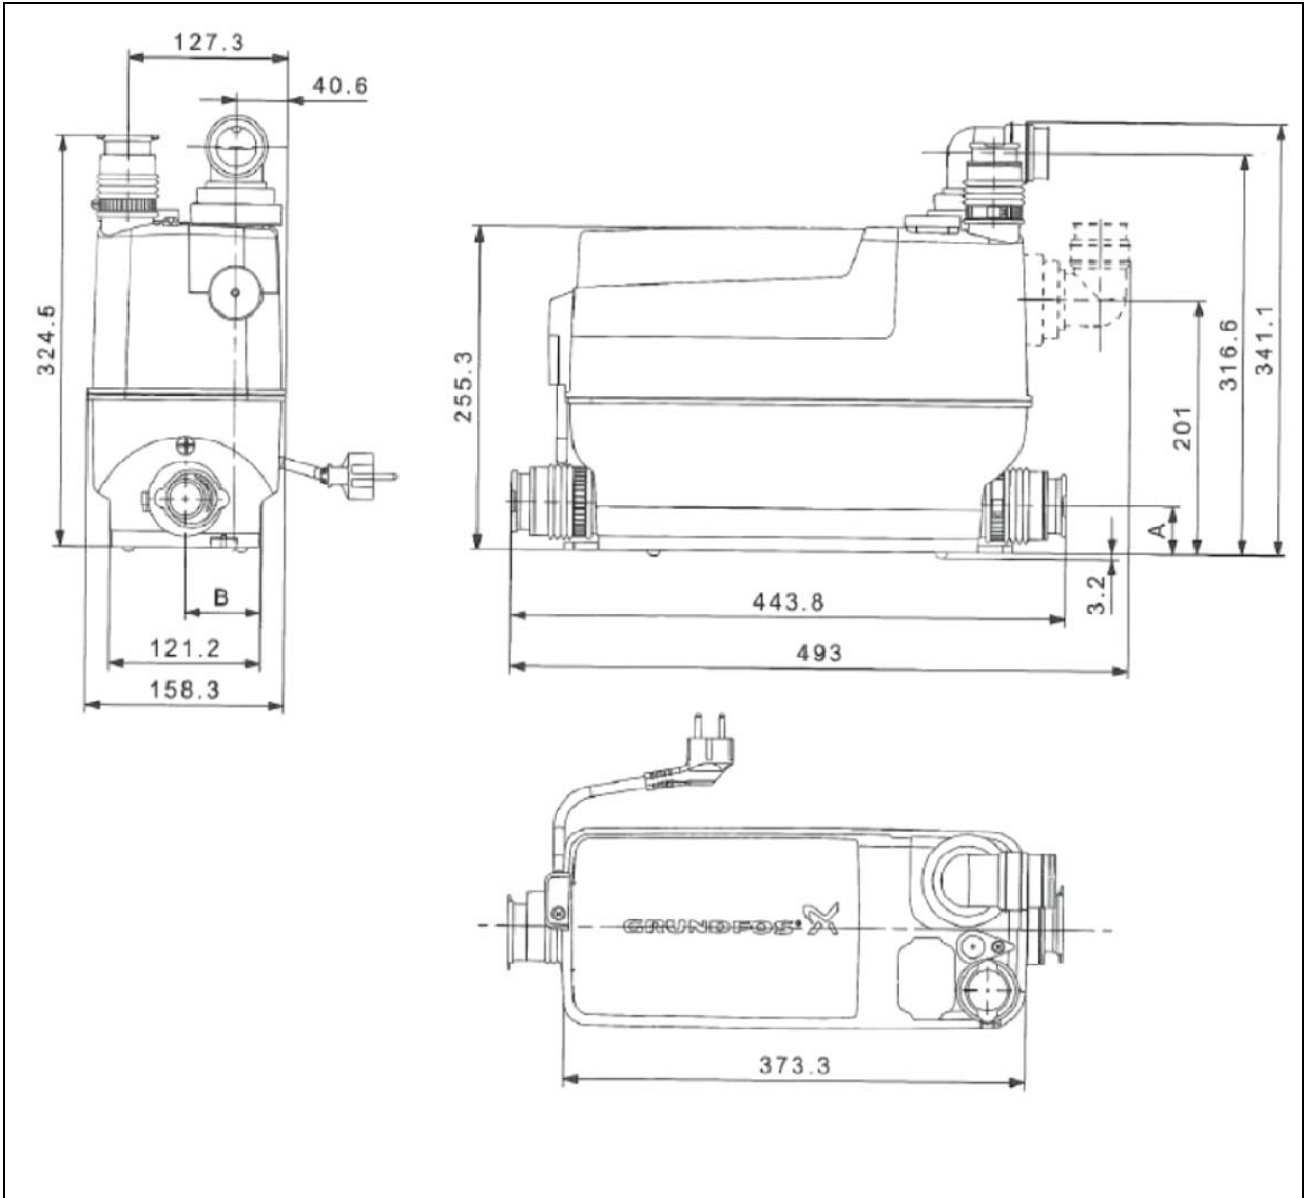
Габаритный чертеж насосной установки SOLOLIFT 2 C-3
